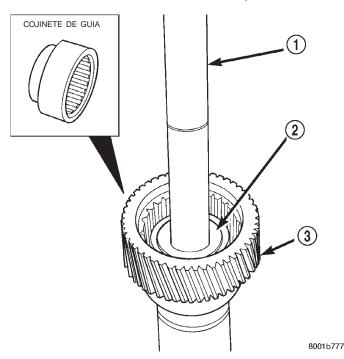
Instalación del cojinete de guía del engranaje impulsor
